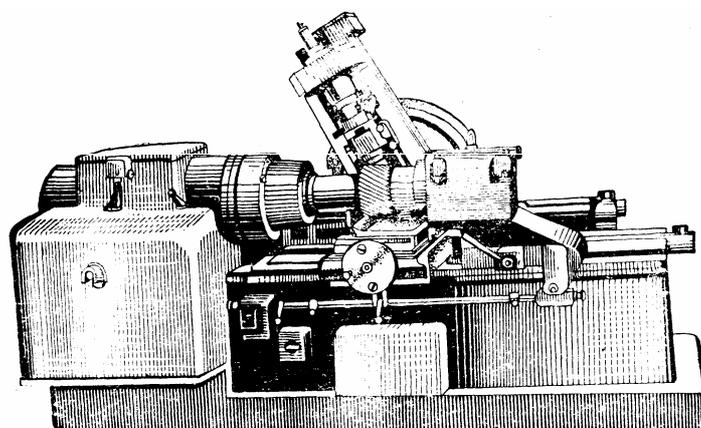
Горизонтальный зубофрезерный станок без люнетов
